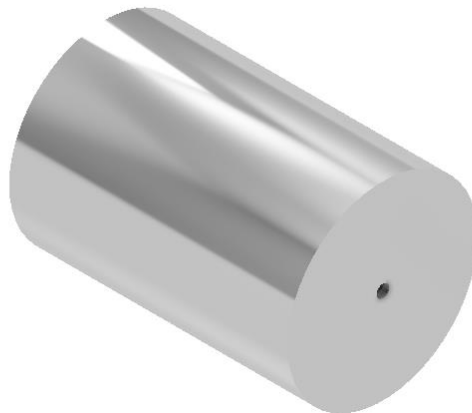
Τρισδιάστατη απεικόνιση αποστολής 53
